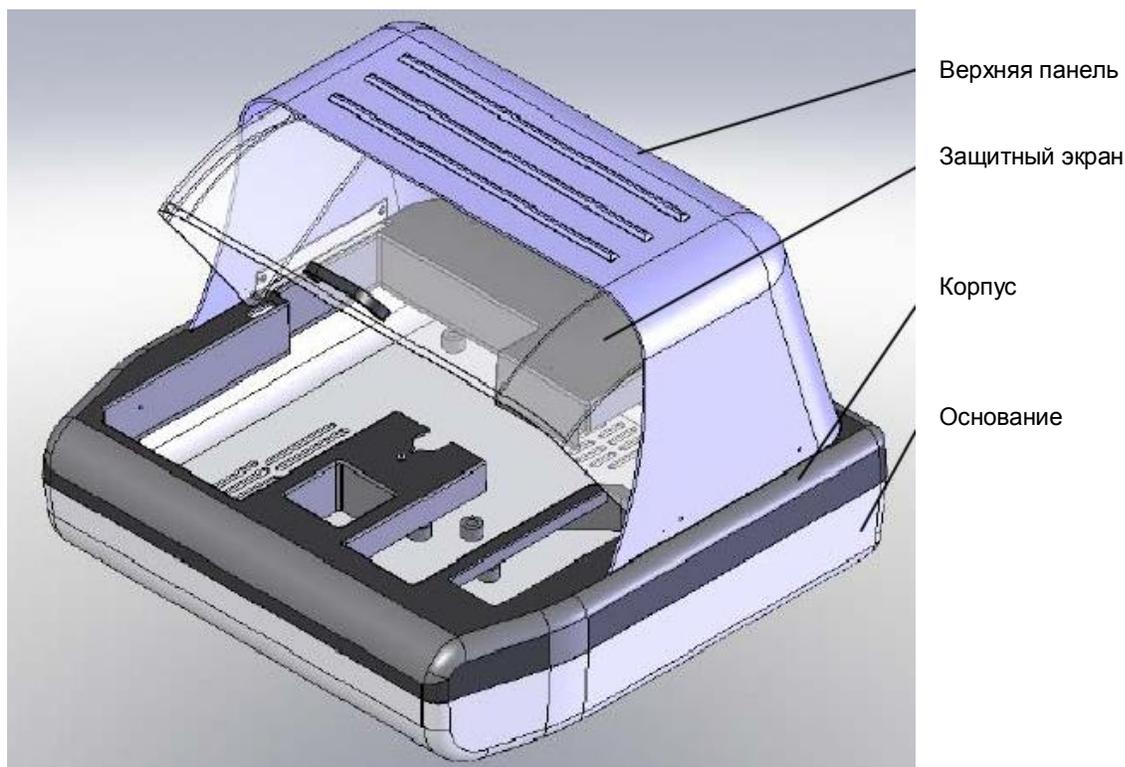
1. Внешний вид прибора, вид спереди
